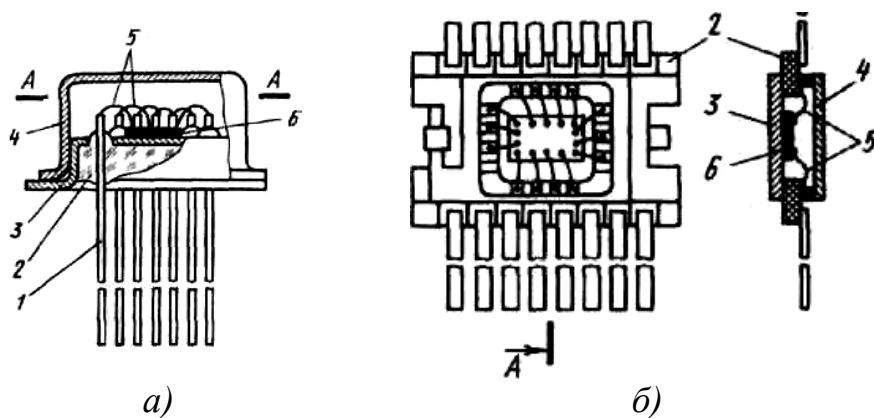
Полупроводниковая интегральная микросхема: *а* - в металлостеклянном корпусе, *б* - в металлокерамическом корпусе; 1 - внешние выводы; 2 – изолятор; 3 - основание корпуса; 4 - крышка корпуса; 5 - соединительные проводники; 6 - кристалл микросхемы
